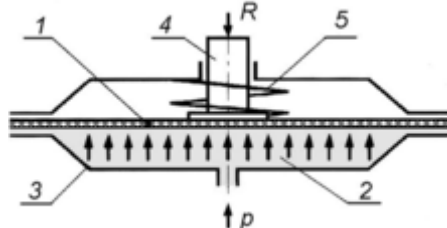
Виконавчий механізм на базі плоскої еластичної мембрани: 1 - диск мембрани; 2 - камера тиску; 3 - корпус; 4 - шток; 5 – пружина
